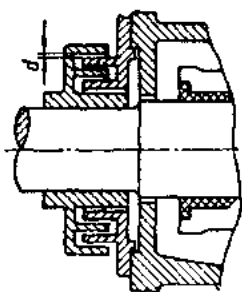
适合于电动机和发电机的滑动轴承，球轴承或滚柱轴承的迷宫式防爆密封装置
